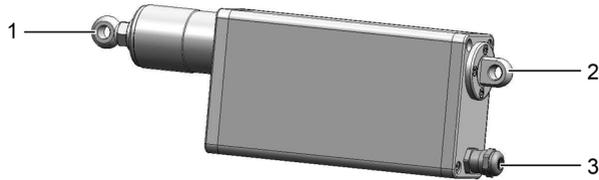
Linearantrieb Junior 1E-VA mit Anschlusskabel
